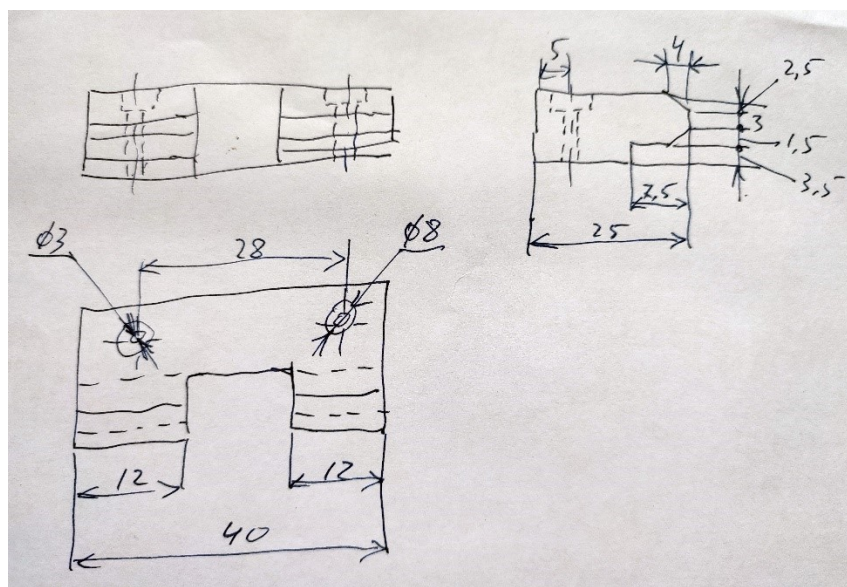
Эскиз детали «Каретка стеклоподъёмника»
